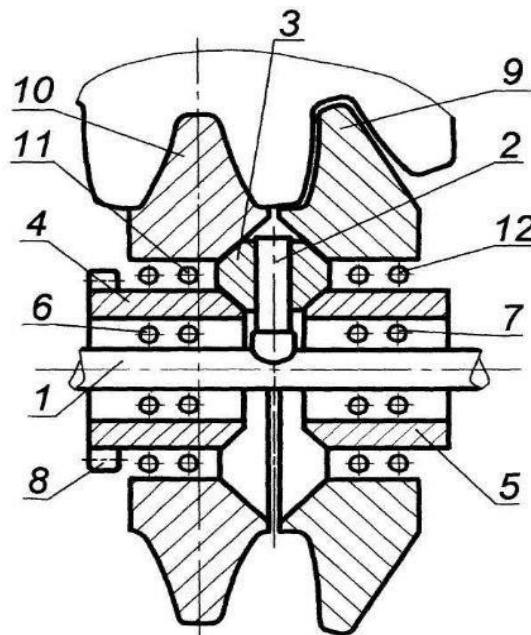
Пристрій для нарізання зубчастих коліс та шліцьових поверхонь
